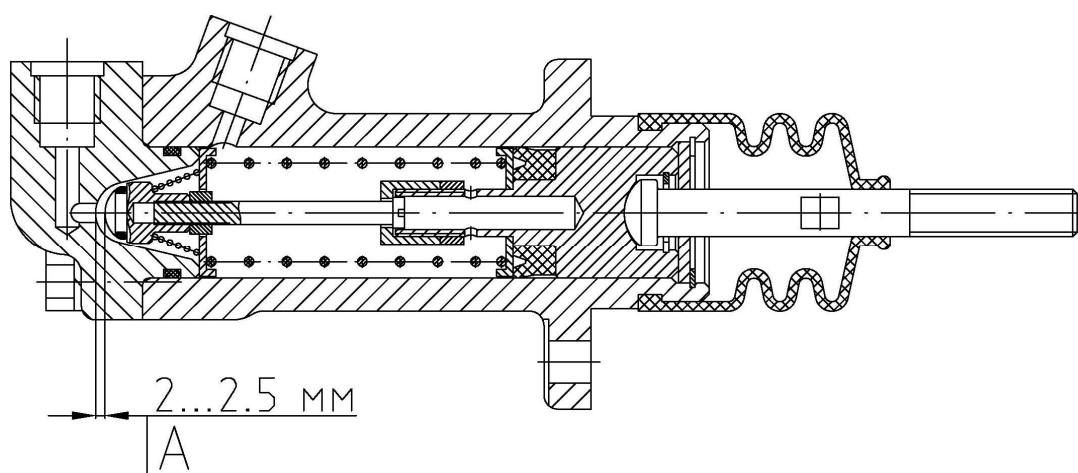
Цилиндр главный 2022-1602810
